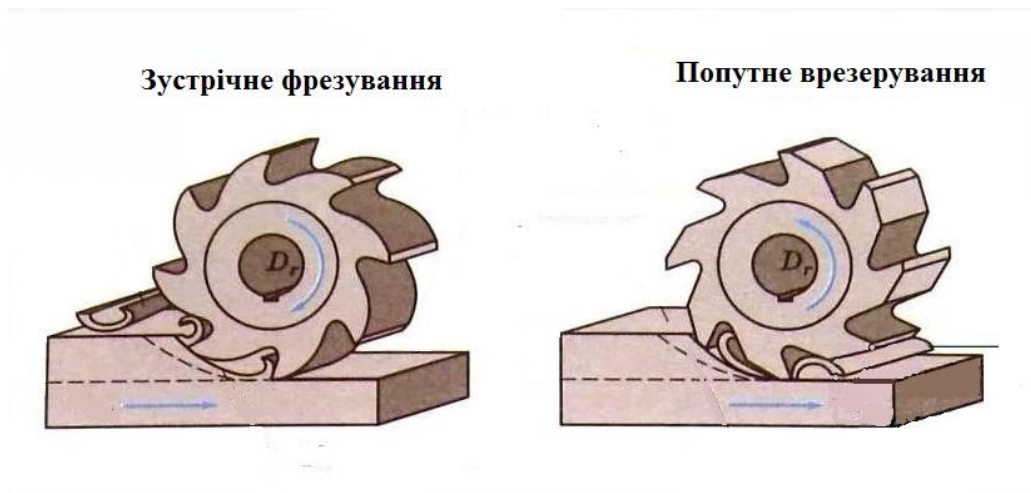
Напрямок подачі та обертання фрези при попутному та зустрічному видах фрезерування
